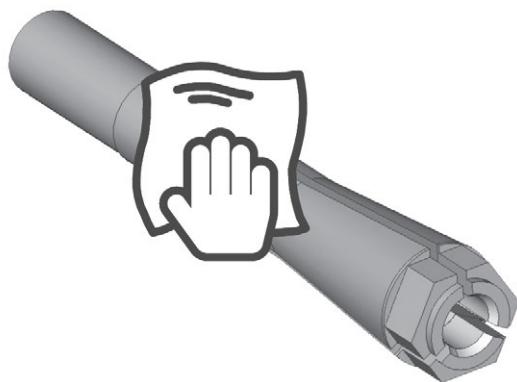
PULIZIA DI TUTTA LA SUPERFICIE ESTERNA DELLA PINZA DI SERRAGGIO CON UN PANNO
